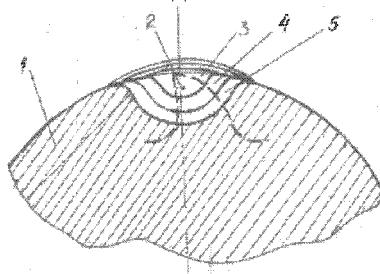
Схема расположения режущего зуба в наплавленном металле, где 1 – заготовка инструмента; 2 – конфигурация режущего зуба; 3,4,5 – форма канавки, в зависимости от высоты наплавляемой части зуба.
